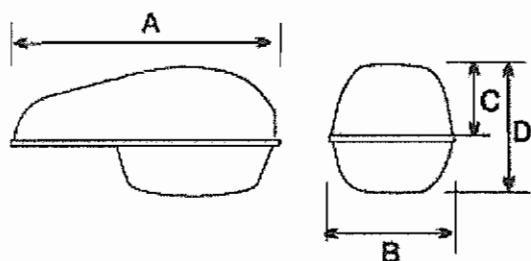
Габаритные размеры светильников серий 99, 97, 77
